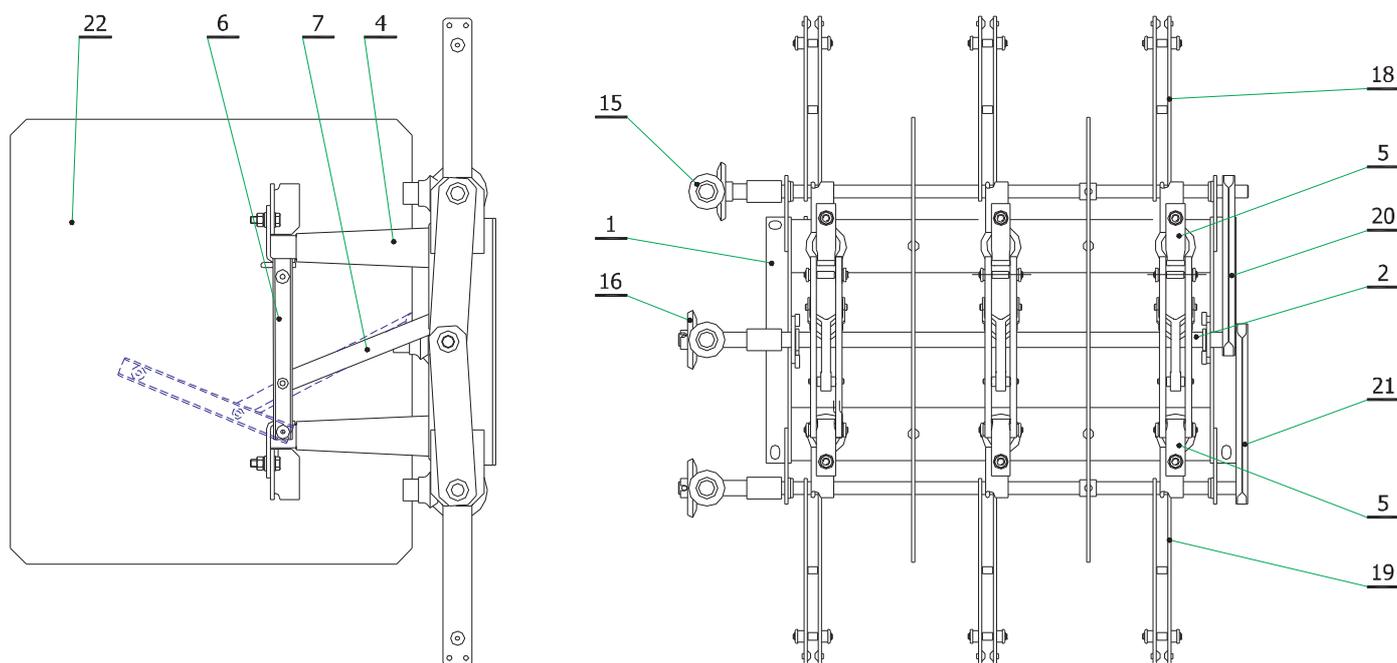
Разъединитель внутренней установки серии OW-12/8/Z/UD/UG (12 кВ, 800 А)
